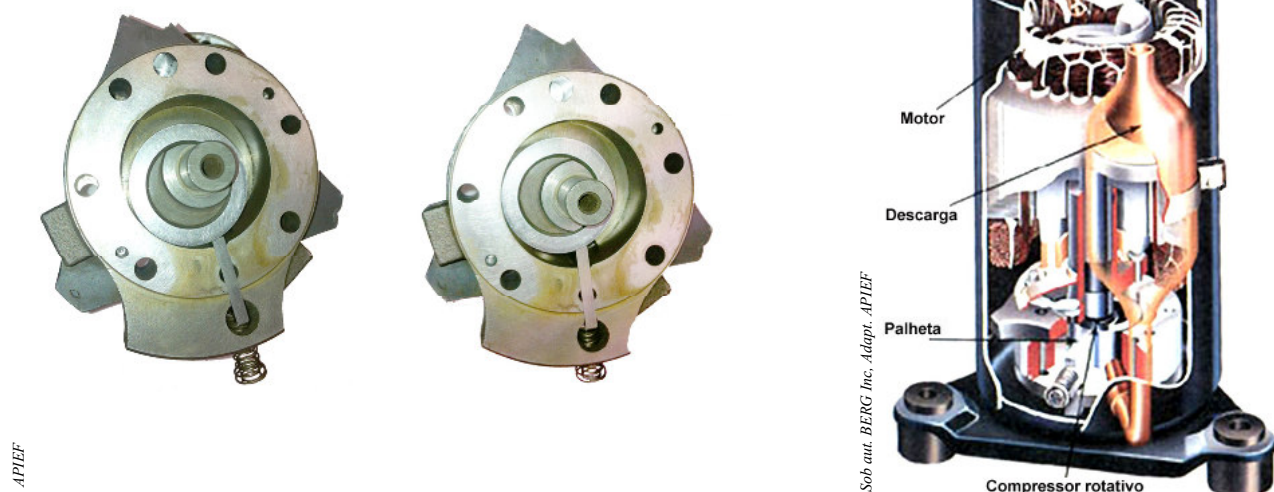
Compressor rotativo de palheta única (duas posições do rotor e corte)
